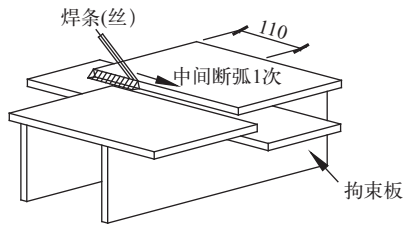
搭接角焊缝试件形式、尺寸和试样取样位置示意
